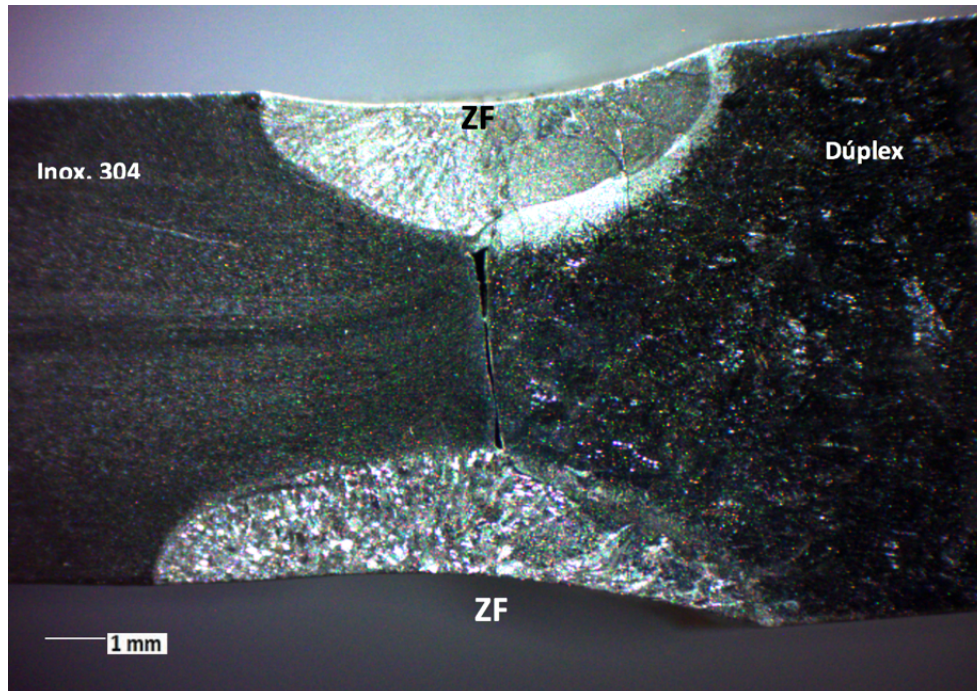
Soldadura disímil realizada a 80 A, vista en microscopio estereográfico. (ZF=zona de fusión)
